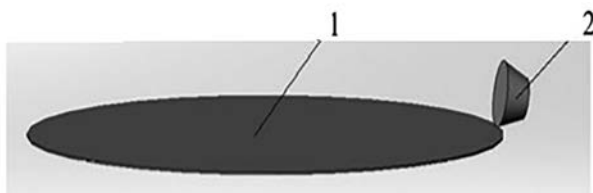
Упрощенная схема лезвийной обработки пластины резцом: 1 — пластина; 2 — резец
